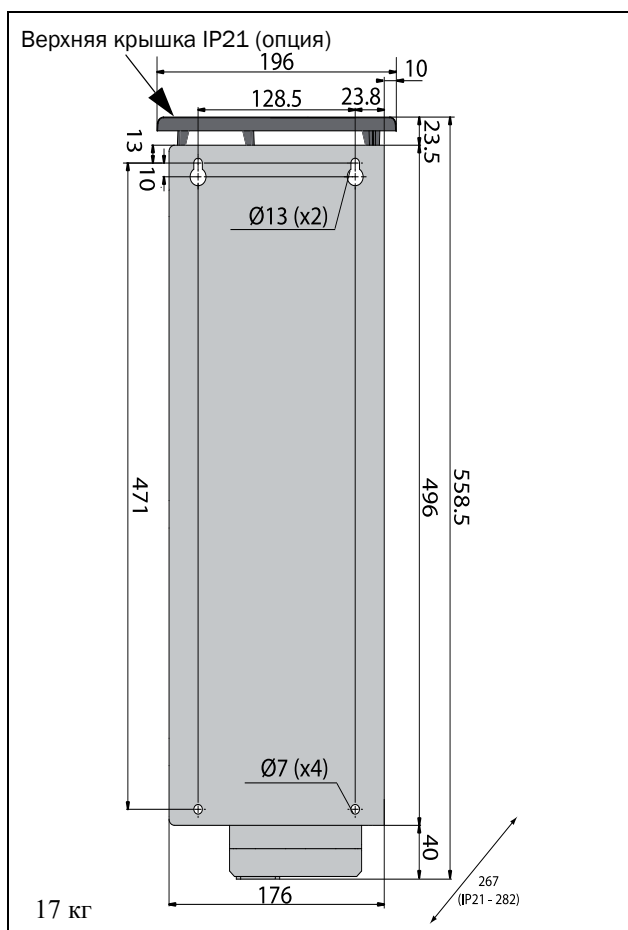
Устройство Emotron FDU моделей 48-025 – 48-045 (типоразмер корпуса C2), вид сзади.
